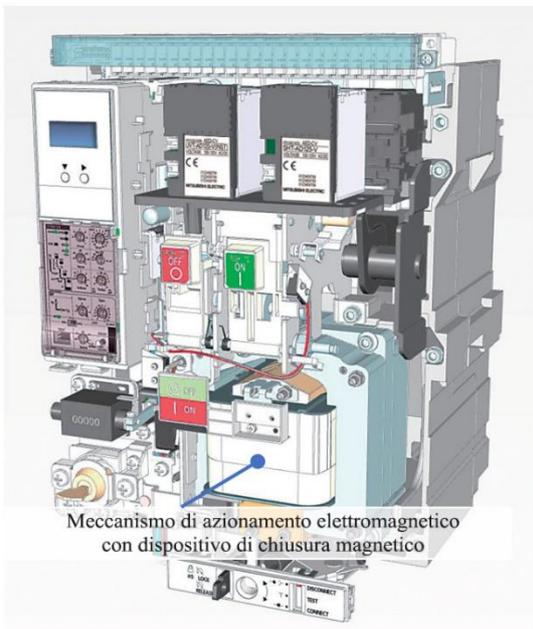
Struttura interna dell'interruttore aperto di bassa tensione
